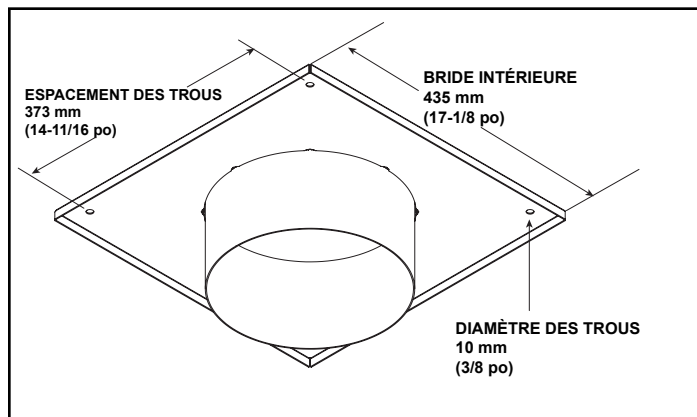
D.2 Dimensions du collier de cheminée de 25 cm (10 po) (RS14)
